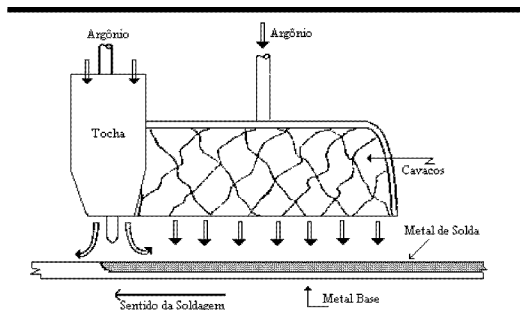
Dispositivo para Soldagem TIG do Titânio.
